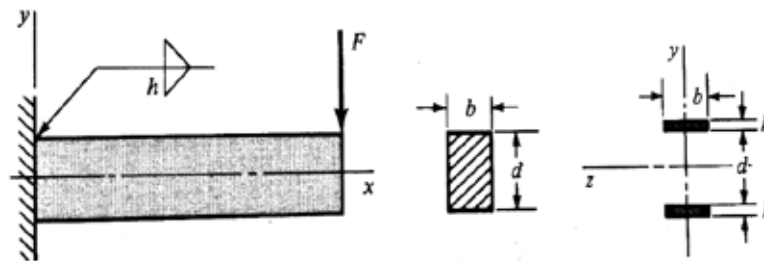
Viga de sección cuadrada unido por soldadura.
